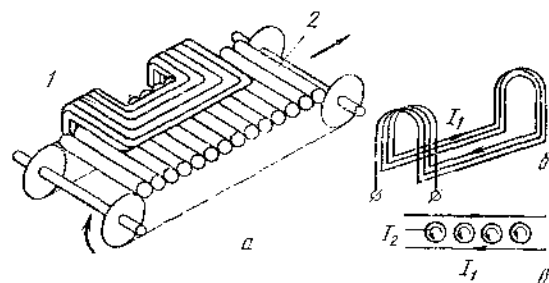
Шелевой индуктор для нагрева концов цилиндрических заготовок (а) и протекание тока в индукторе (б) и в заготовках (в)
